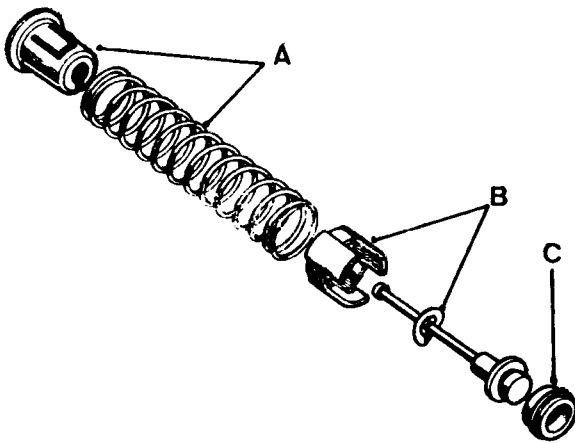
12 - Desmontaje de la válvula del cilindro.
